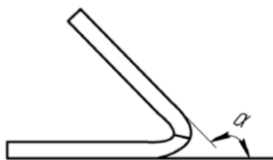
Схема определения угла  $\alpha$  изгиба сварного соединения
